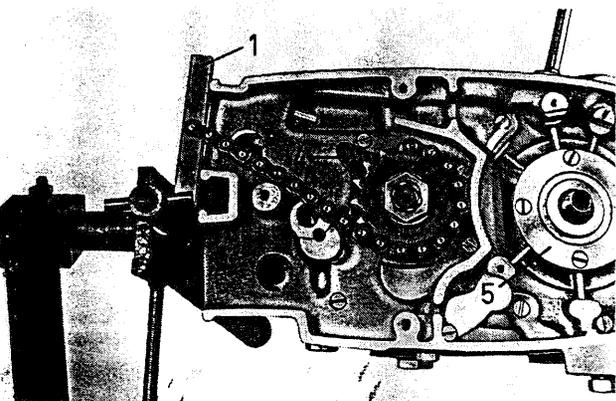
Démontant la roue dentée à chaîne dans les engrenages
